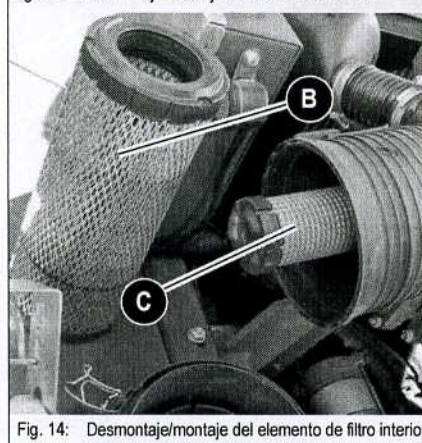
Desmontaje/montaje del elemento de filtro interior
